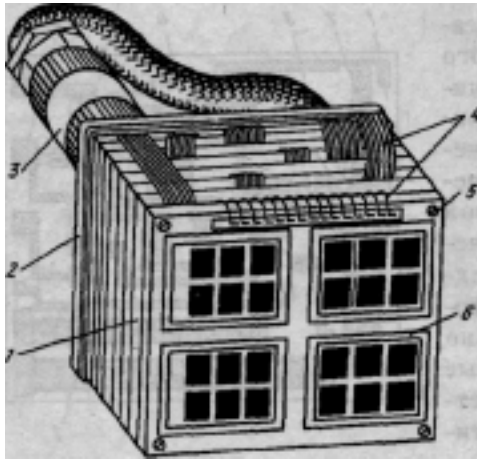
Конструкция герметичного блока РЭС IV поколения (корпус условно снят):
